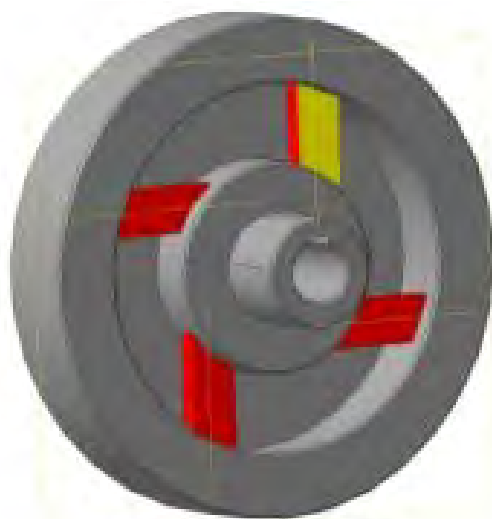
Схема торцевої установки пружних елементів [218]
